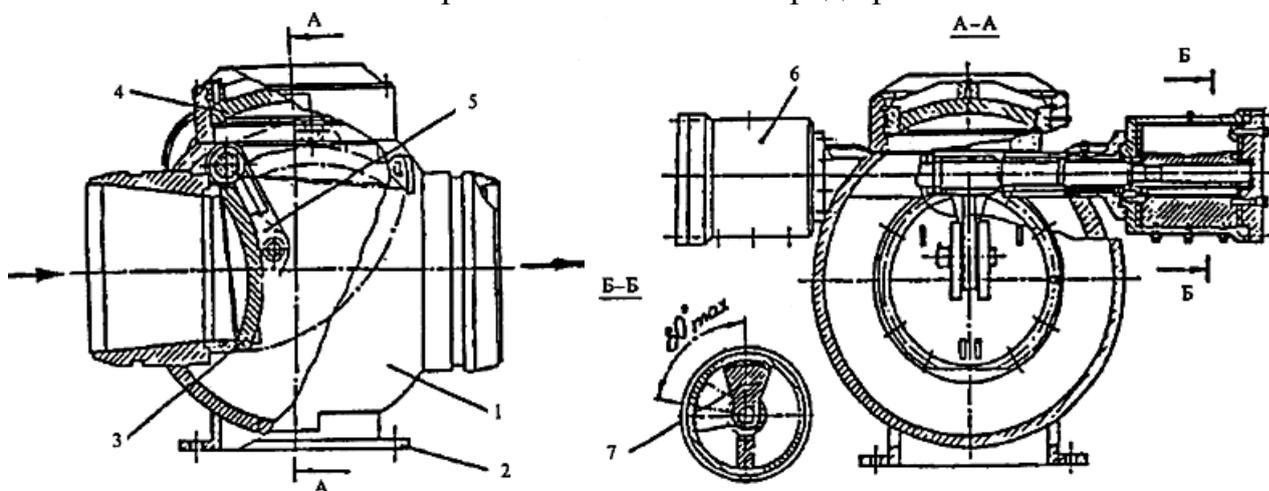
Обратный поворотный клапан с пневматическим демпфером:
